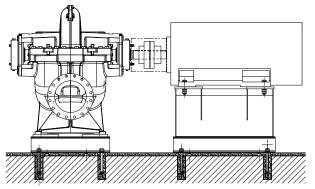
4 E: насос и привод на отдельных фундаментных плитах
